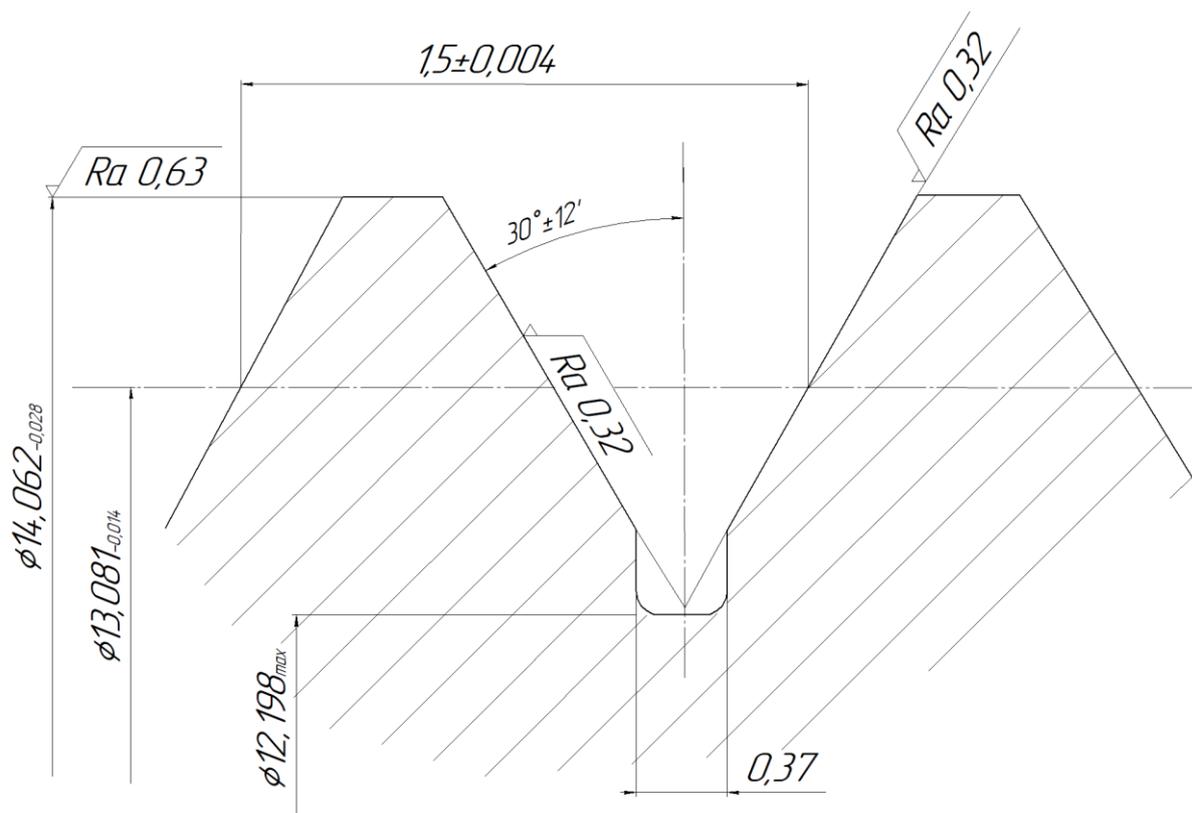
Пример оформления профиля резьбового проходного калибра – пробки
